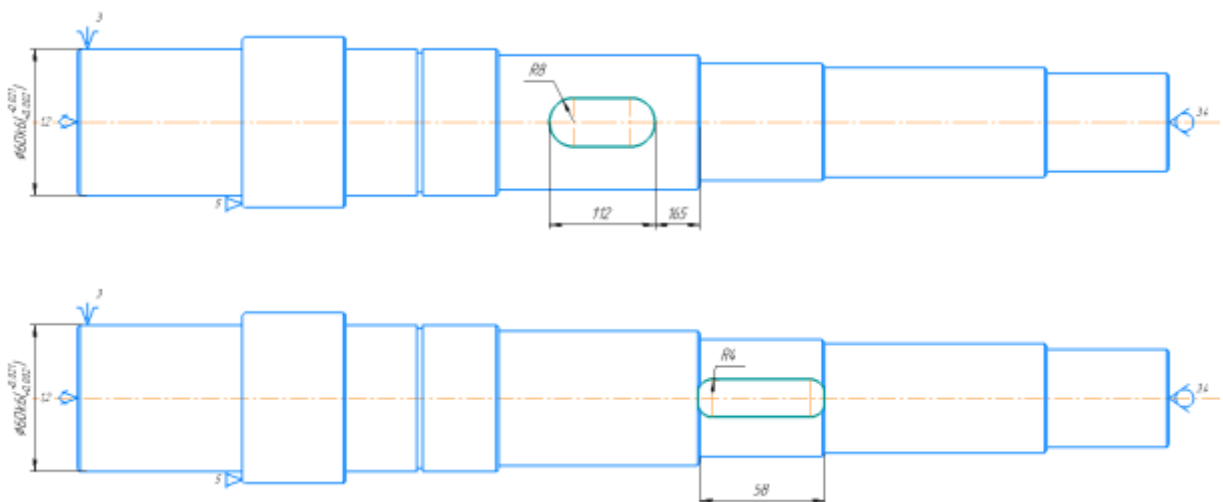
Базування та закріплення заготовки на операції 025.
